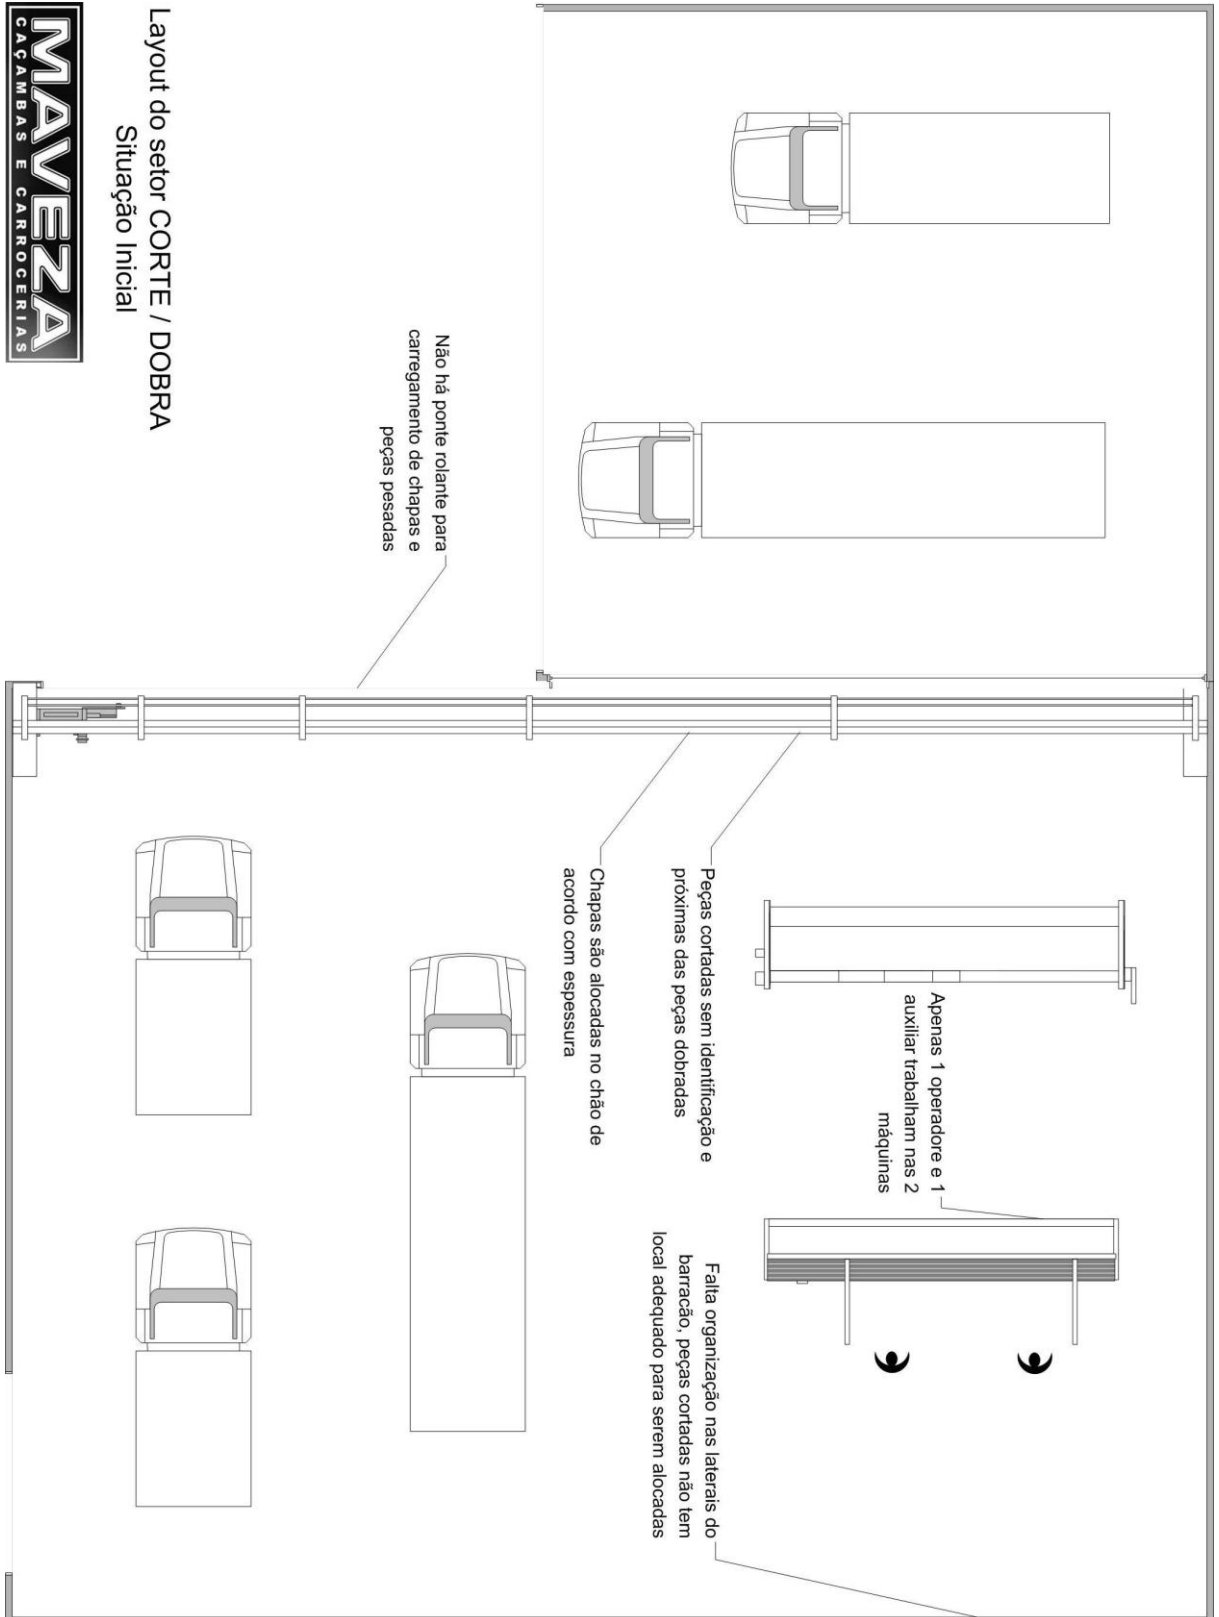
Layout inicial do Corte/Dobra e Montagem
